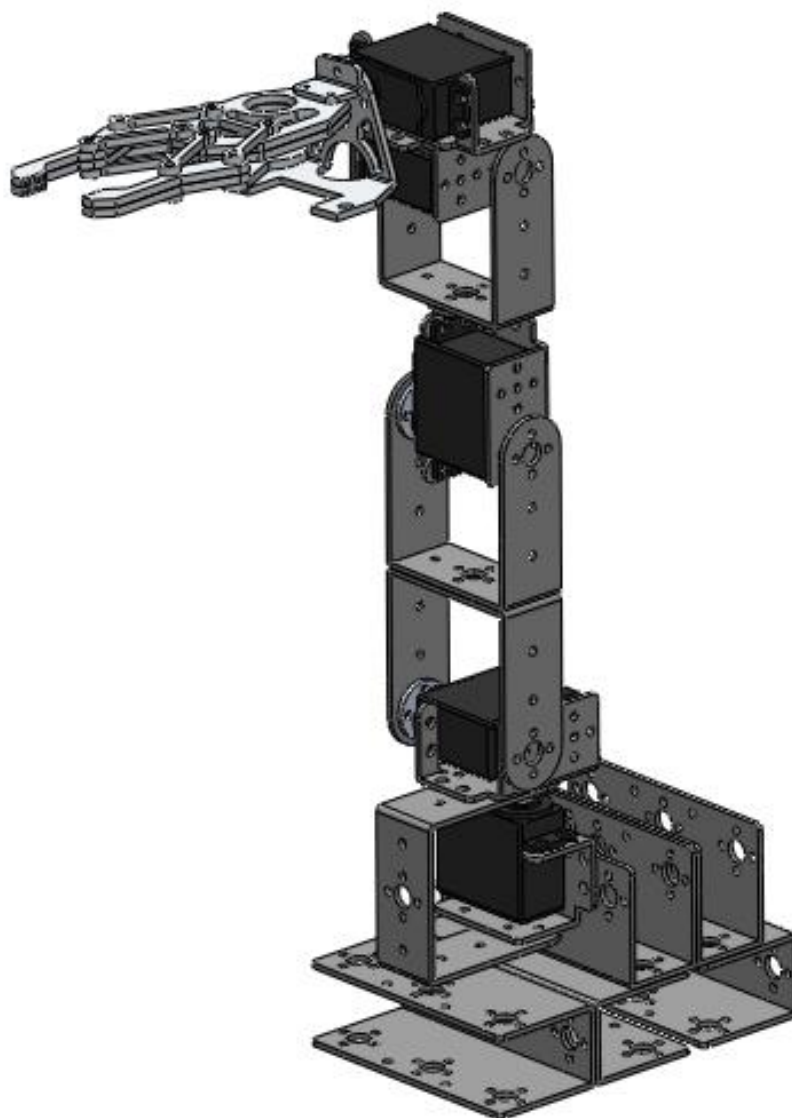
Diseño del Brazo Robot en Solidworks Vista Isometrica
